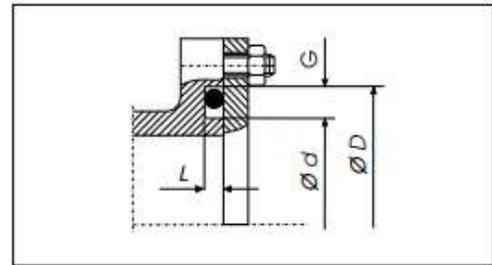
Cotas principales a tener en cuenta para el diseño de alojamientos para o'ring.
